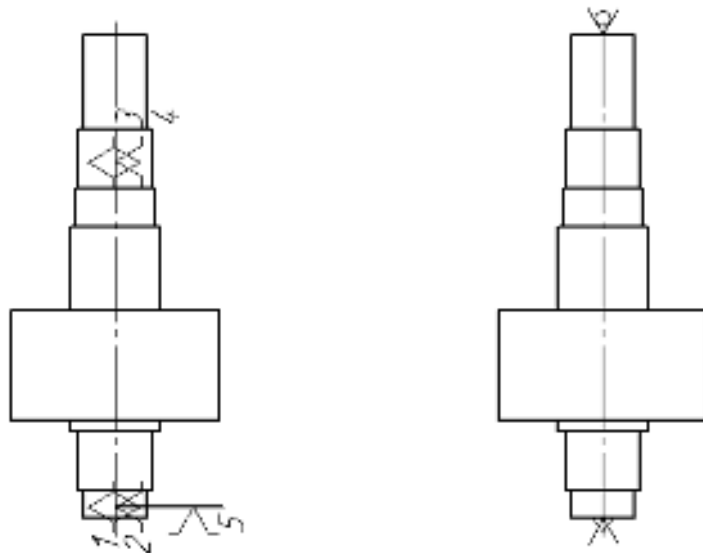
Схема базування і закріплення деталі на зубофрезерній операції
